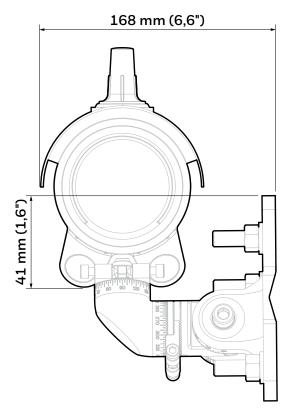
Vista generale e dimensioni della staffa di montaggio universale
